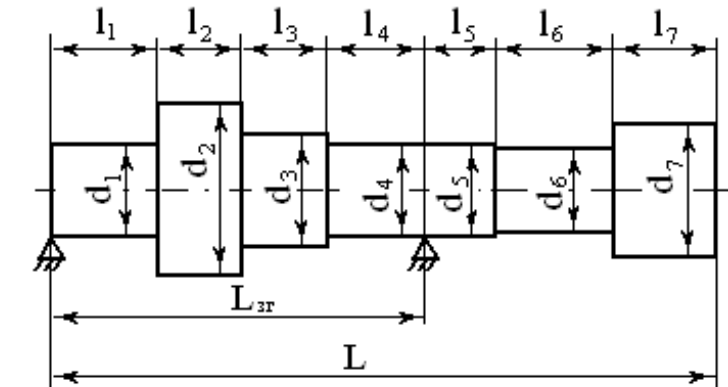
Схема зведеної конструкції вала з установленими деталями на валу з натягом
